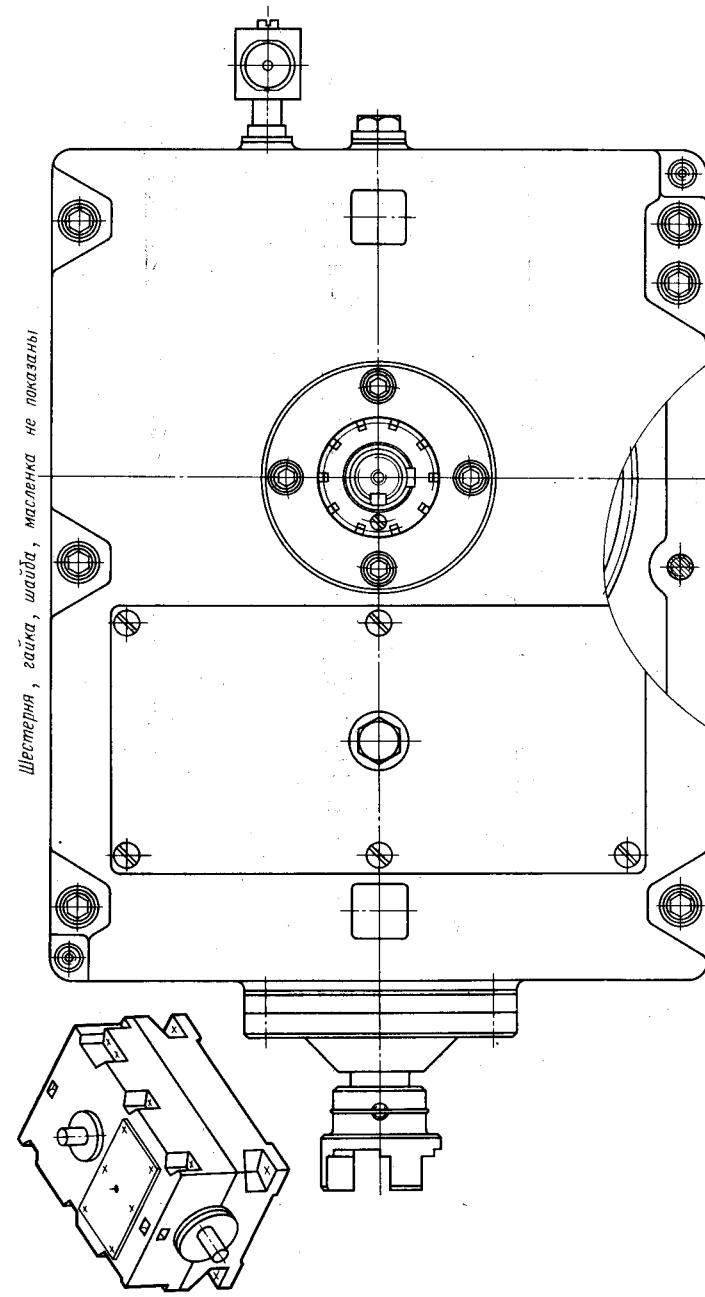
Редуктор конический одноступенчатый с вертикальным тихоходным валом
